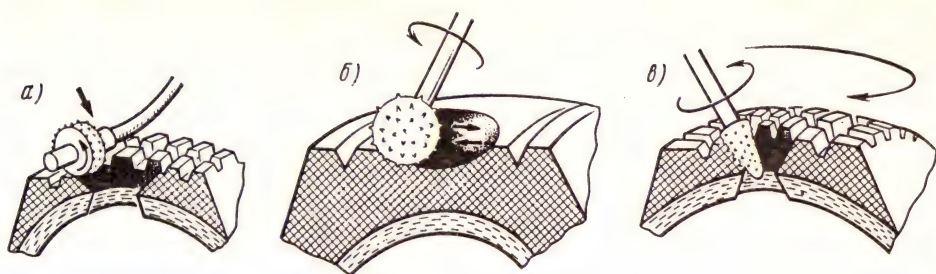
Способы шероховки поврежденных мест покрышки:
